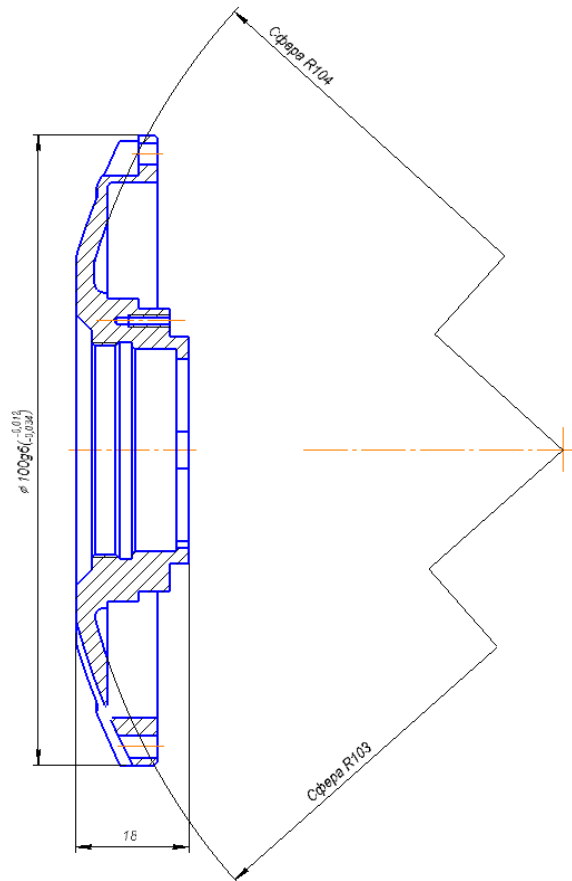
2D модель детали "Корпус опоры 3"
